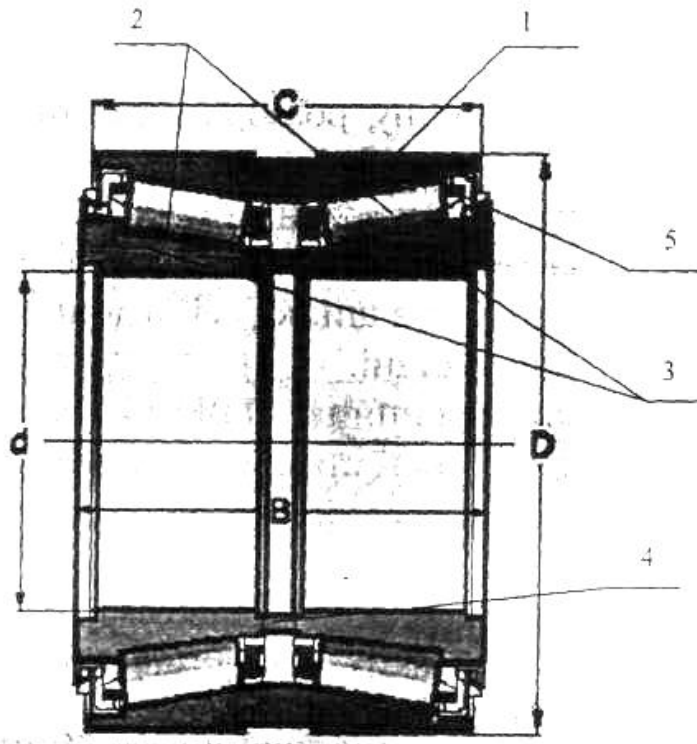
Загальний вигляд конічного підшипника типу ТВУ:
